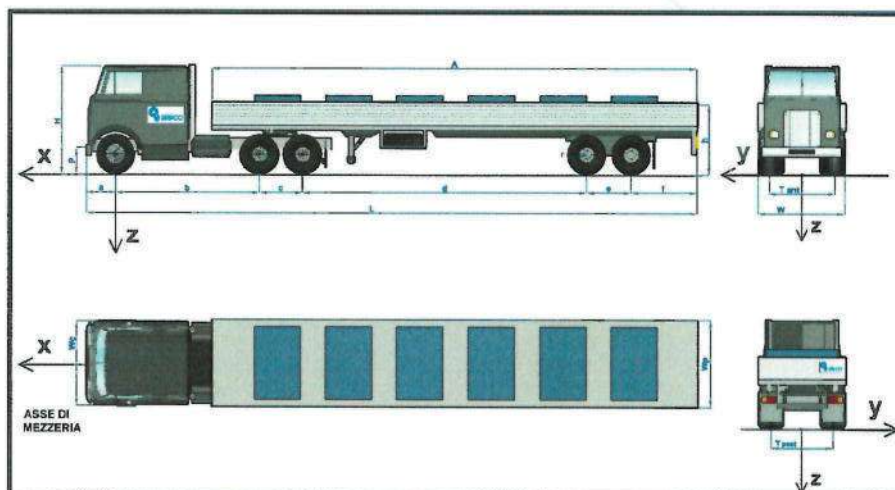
Figure 3 Dimensioni del veicolo – Vehicle dimensions
